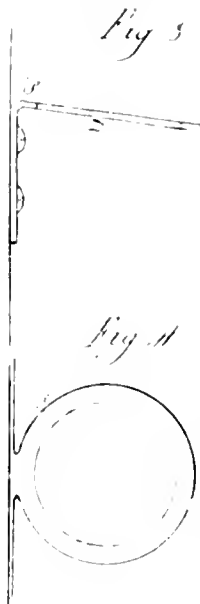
Supports à bouteilles. (183 coupe; 184 plan).
